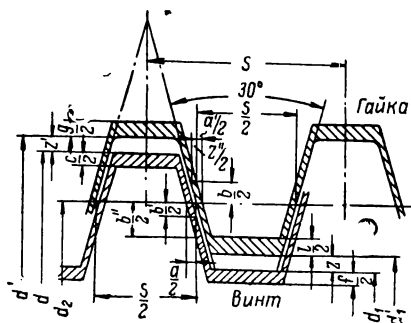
Схема расположения допусков трапецеидальной резьбы.
